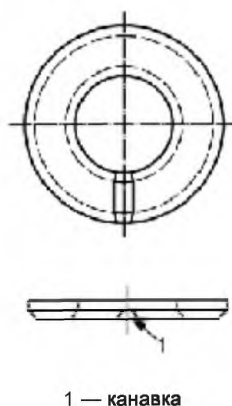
Подготовка шайбы для установки под головку болта:
